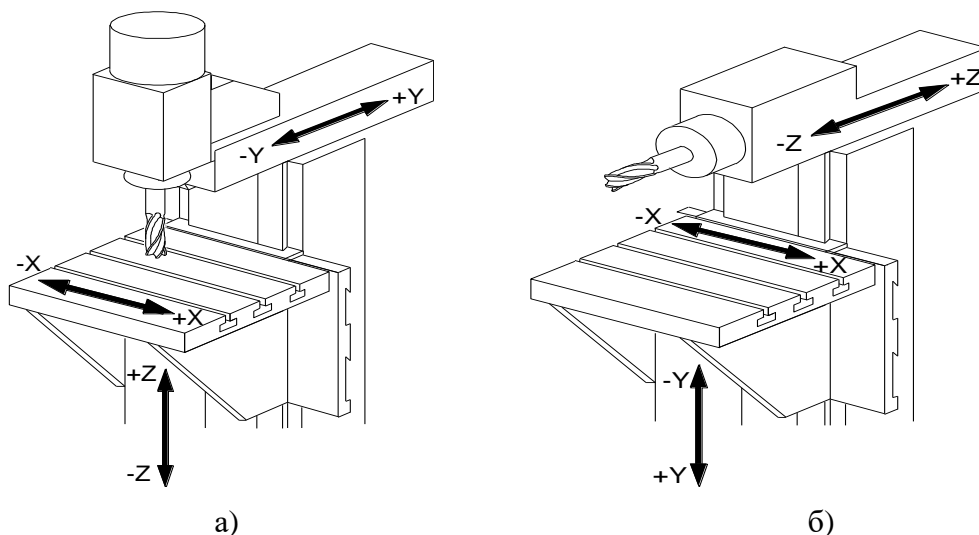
Система координат вертикально-фрезерного верстата (а) і горизонтально-фрезерного верстата (б)
